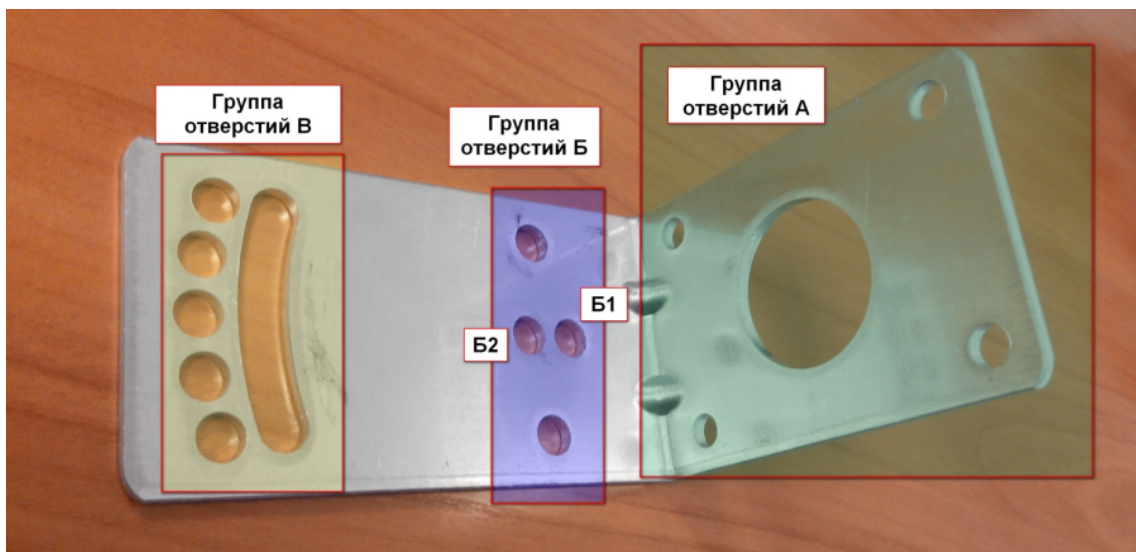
Внешний вид кронштейна с обозначением групп отверстий
